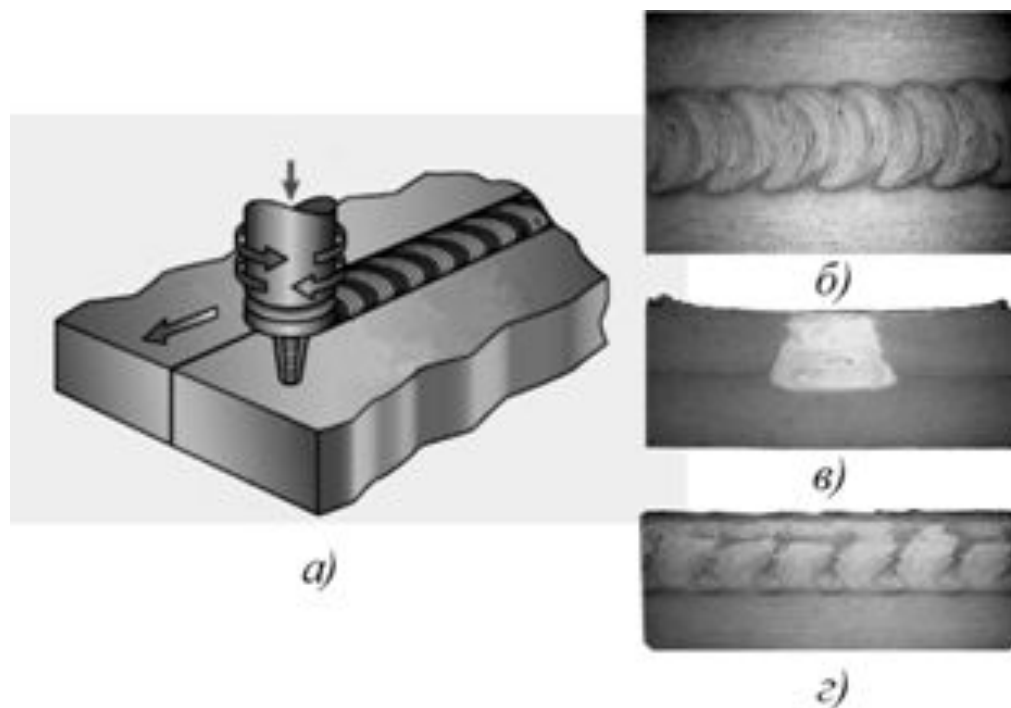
ПСТ с возвратно-вращательным движением инструмента:
